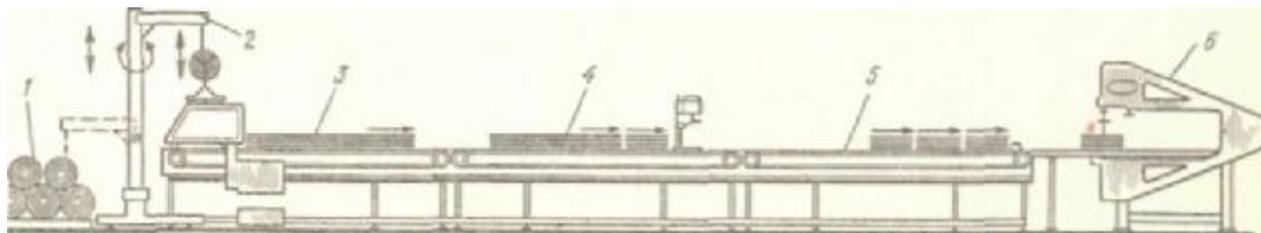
Полуавтоматическая линия по изготовлению заготовок ткани фирмы «Краус и Райхерт»
